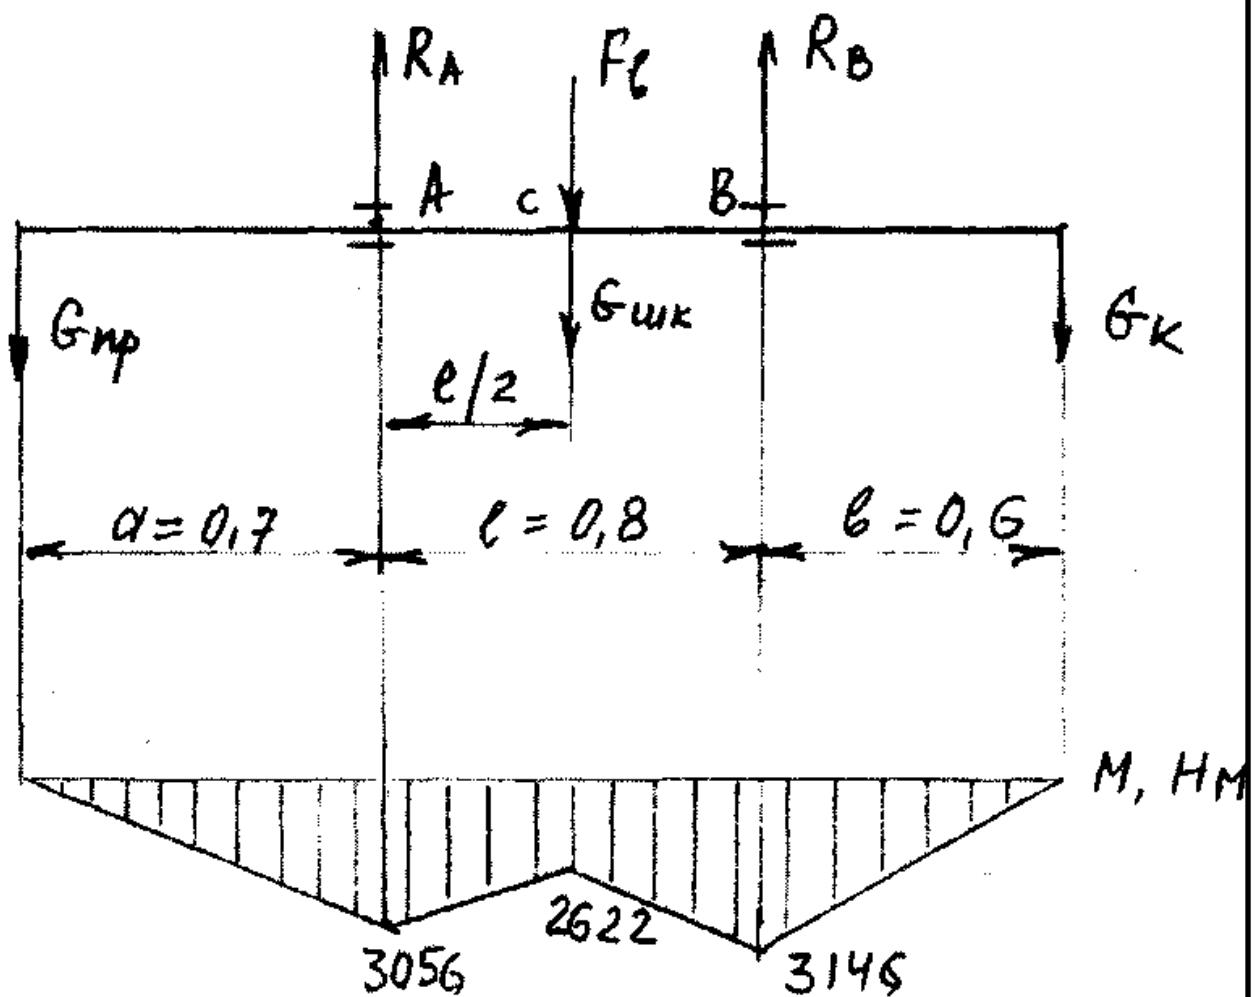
Розрахункова схема та епюри згинання для вала лівого кошика
